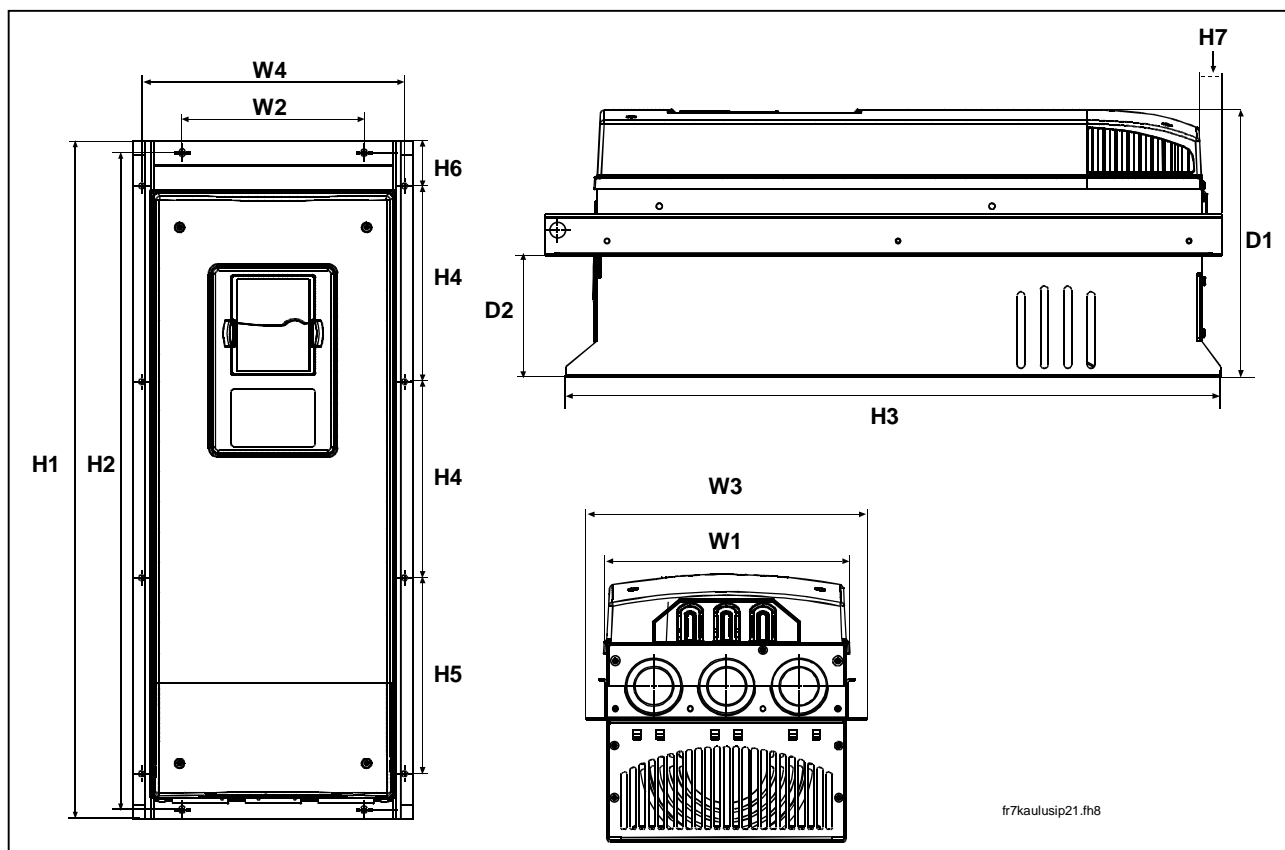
Dimensiuni Vacon NX\_, FR7 și FR8, montare cu flanșă
